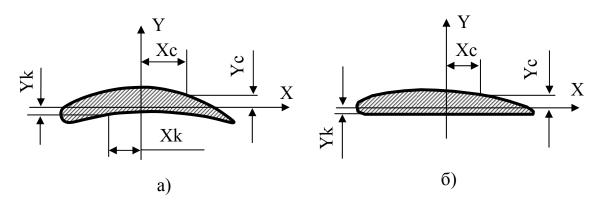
Профиль i-го сечения лопатки: - б— действительный, а — выпрямленный;
